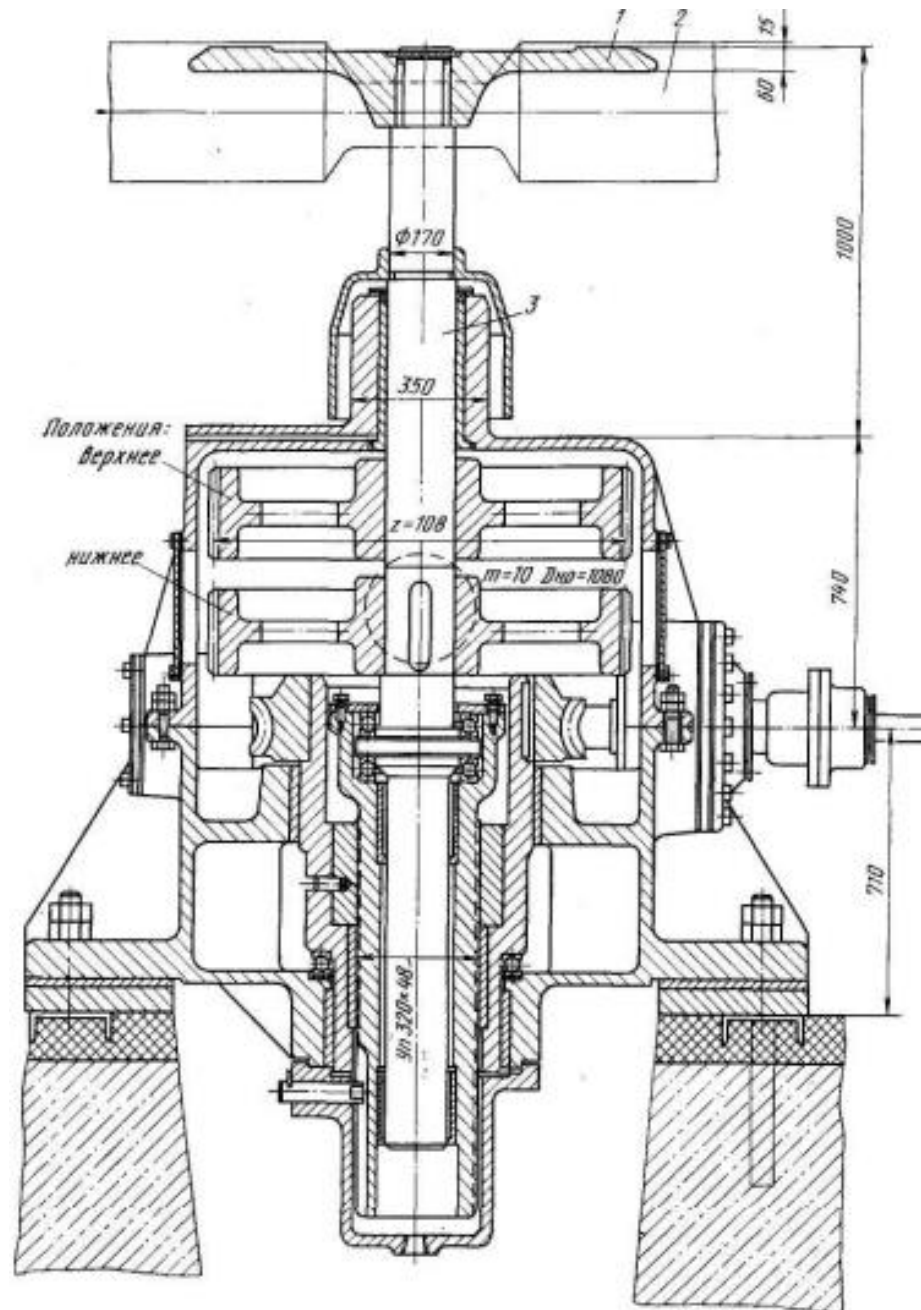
Підйомно-поворотний пристрій у лінії товстолистового стану: 1-хрестовина; 2-ролики; 3-вертикальний вал
